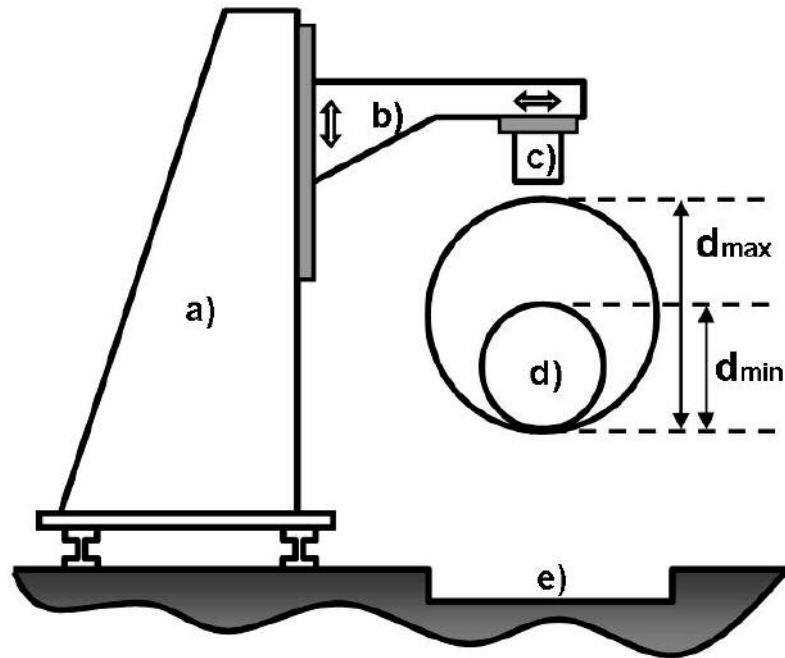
Prüfmechanik für UP-spiralgeschweißte Rohre. a) Maschinenständer; b) Ausleger mit vertikaler Einstellmöglichkeit; c) Prüfkopfhalterungen mit horizontaler Positionseinstellung; d) UP-spiralgeschweißtes Rohr; e) Fundament mit Wasser-Auffangbecken (geschlossener Wasserkreislauf).
